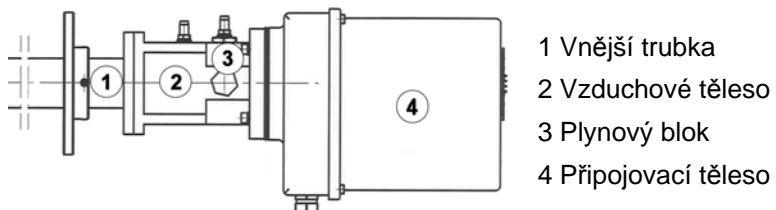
Hlavní části zapalovacího hořáku LAM-TEC GFI
